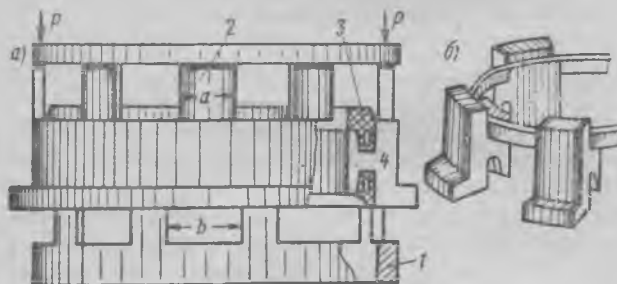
Распрессовка коллектора тягового двигателя УРТ-110:
